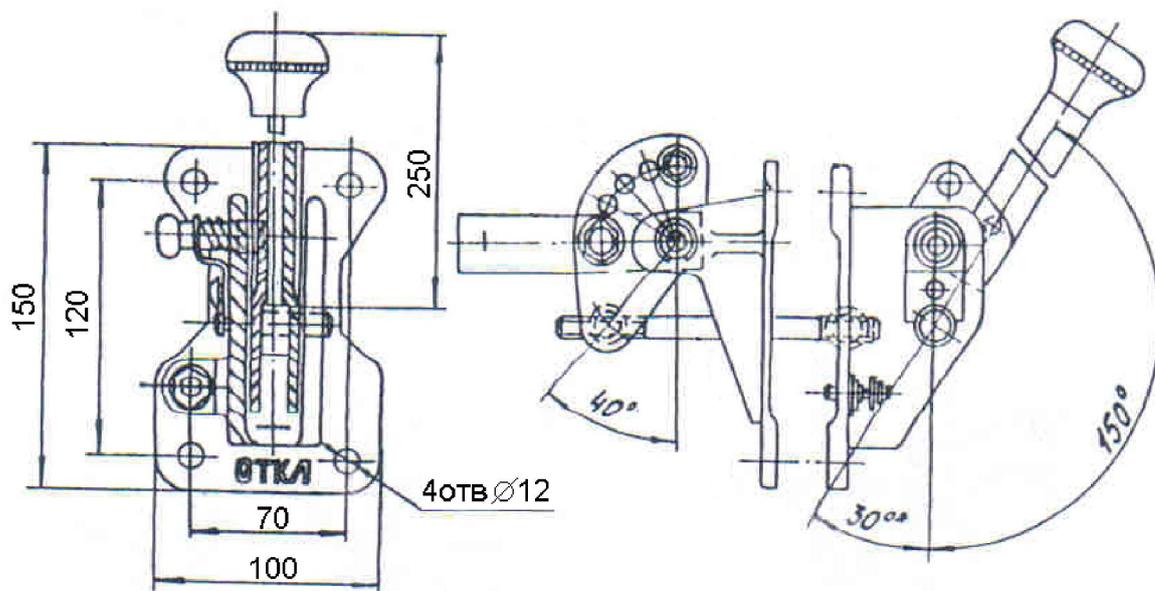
Габаритные размеры привода ПР-10УЗ (масса-2,3кг)
